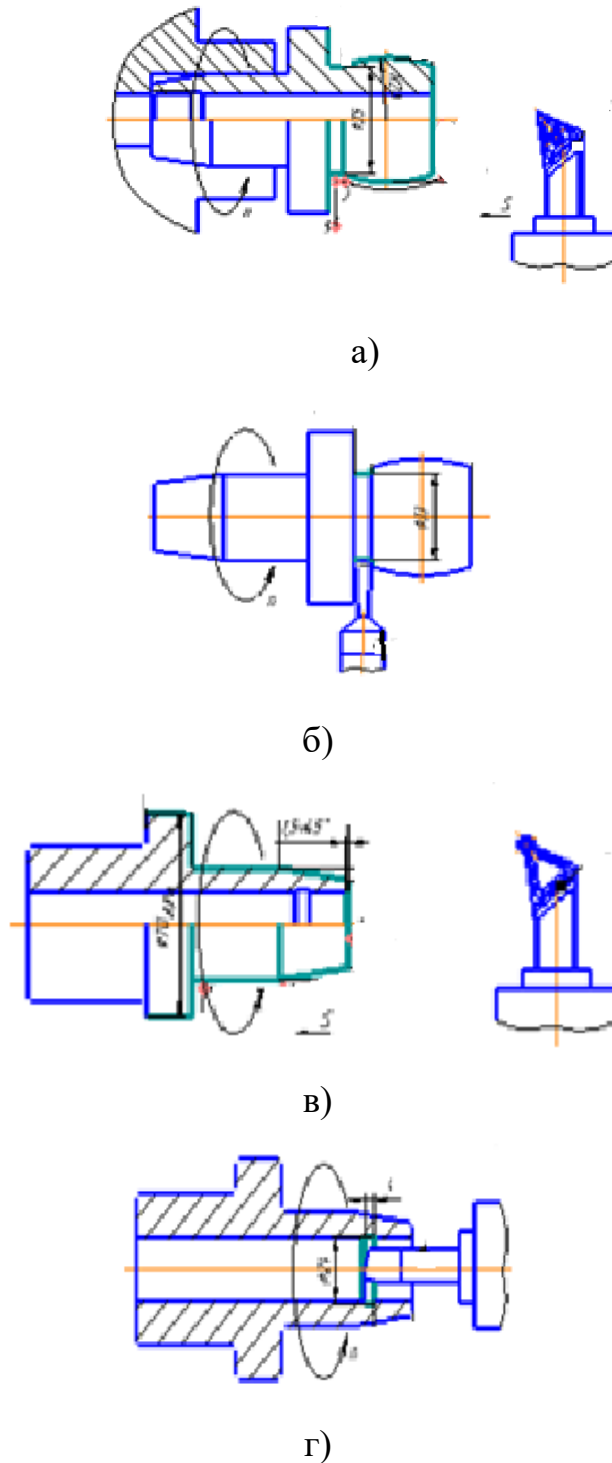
Рухи формоутворення при обробці: а) зовнішньої поверхні; б) канавки; в) конічної і торцевої поверхні; д) внутрішньої поверхні
